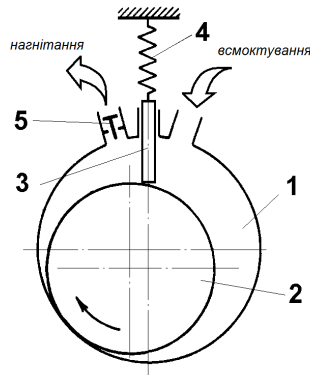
Ротаційний оливнонасос: 1 - циліндр (корпус); 2 - ротор; 3 - лопать; 4 - пружина; 5 - нагнітальний клапан
